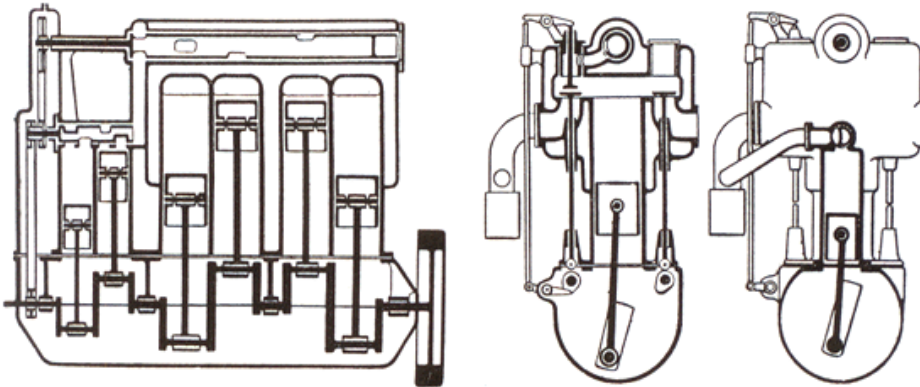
Sobrealimentación del motor por medio de un compresor de émbolos ideado por Birking en 1912.
